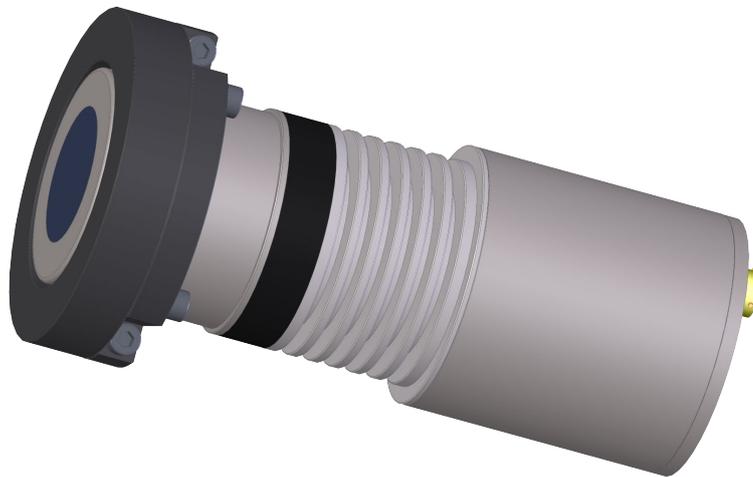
Bague de serrage et plaque de fixation fixées à un Hydro-Mix HT
